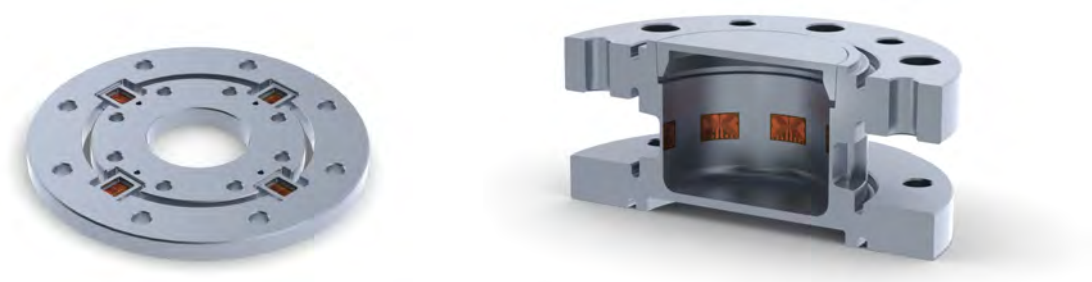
Flanschaufnehmer mit radialem (links) und axialem Scherprinzip (rechts) [KK12].
